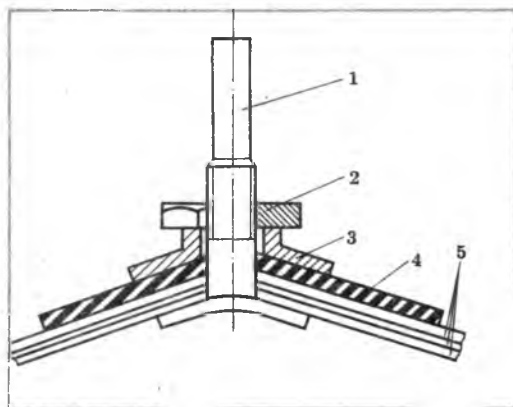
Приспособление для полировки стекол: 1 — металлический стержень (зажимается в дрель); 2 — гайка; 3 — профильная шайба; 4 — резиновый грибок; 5 — фетровые диски
